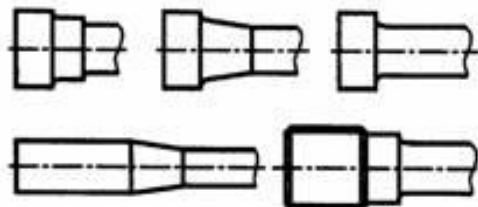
Типы головок цилиндрических образцов для испытаний на растяжение
